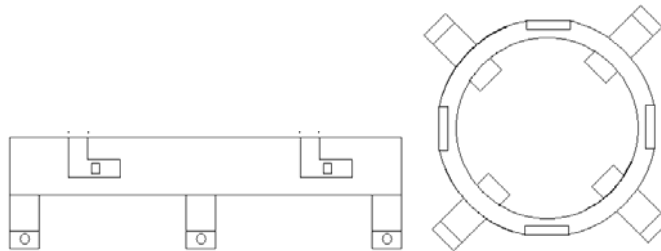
Interfaz Sistema de Suspensión-Socket del lado del socket. Izquierda vista frontal, derecha vista superior
